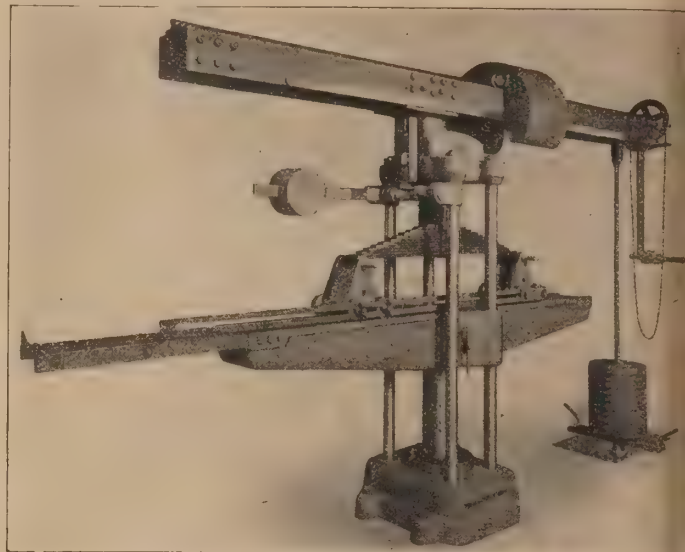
Federprüfmaschine für Blatt- und Spiralfedern.
